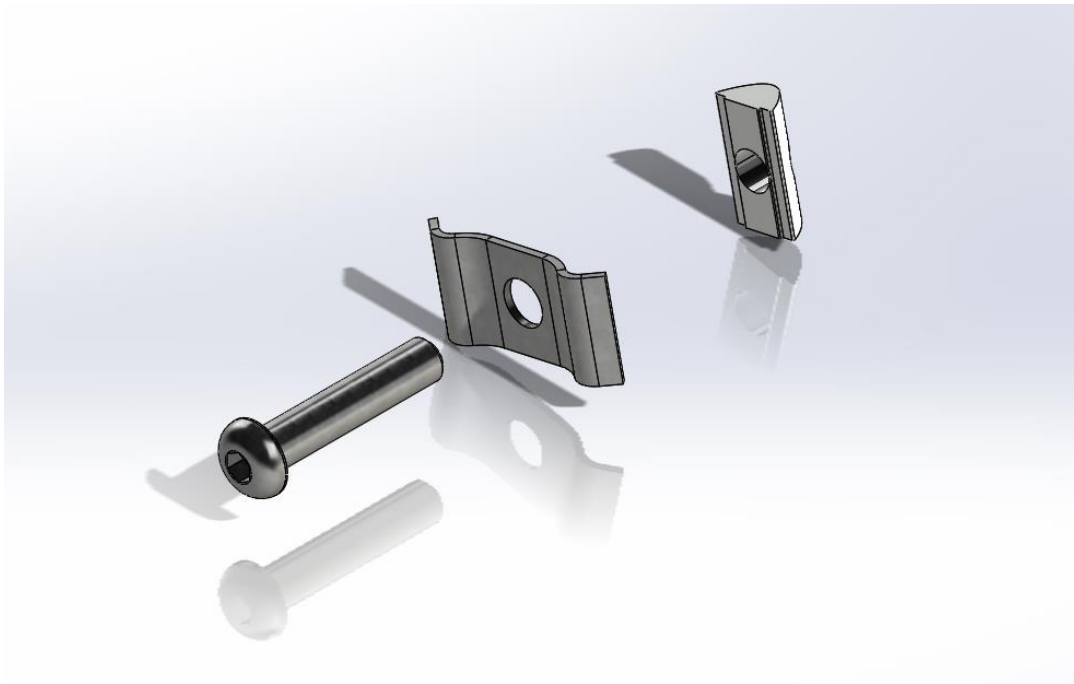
Vista explosionada de conjunto atornillado para emparrillado.
